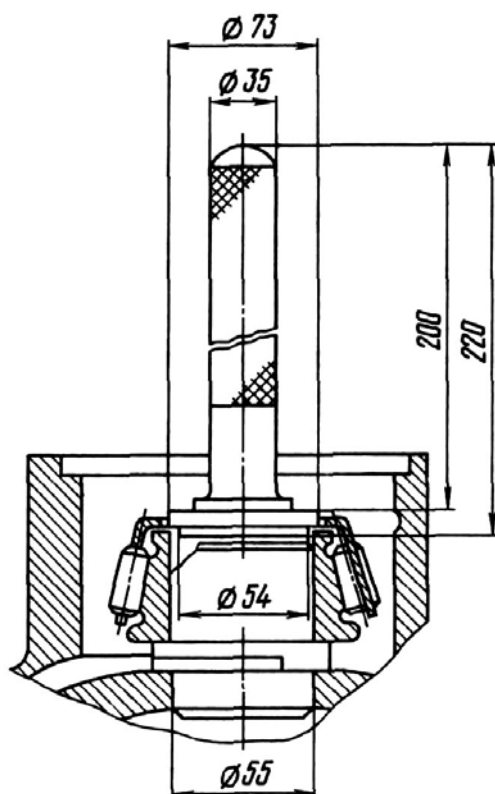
Напрессовка внутренней обоймы подшипника на шкворень шаровой опоры
